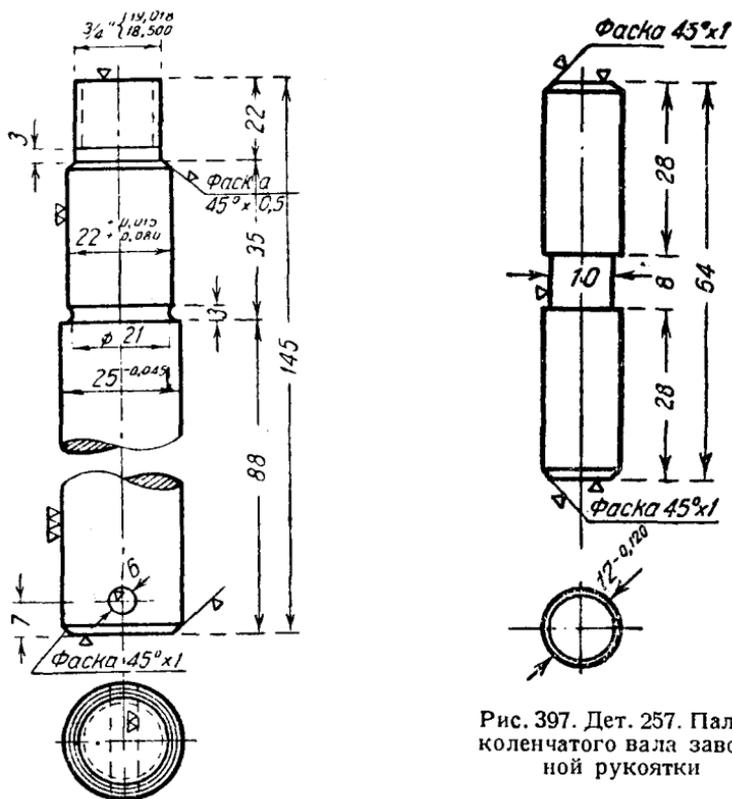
Дет. 257. Палец коленчатого вала заводной рукоятки
